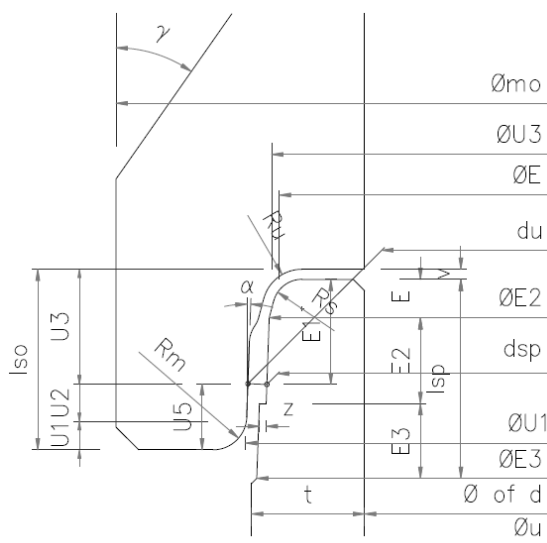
Exemple dimensions emboîtement mâle-femelle avec joint glissant
